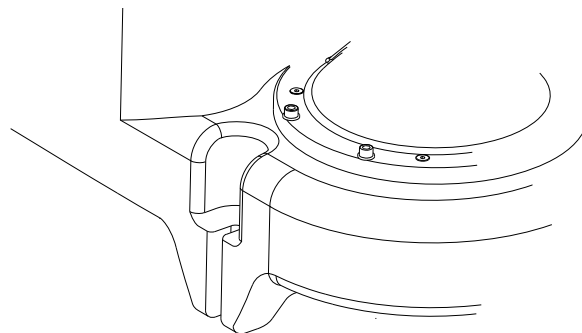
Точка крепления для монтажа резервуара на фундаменте
